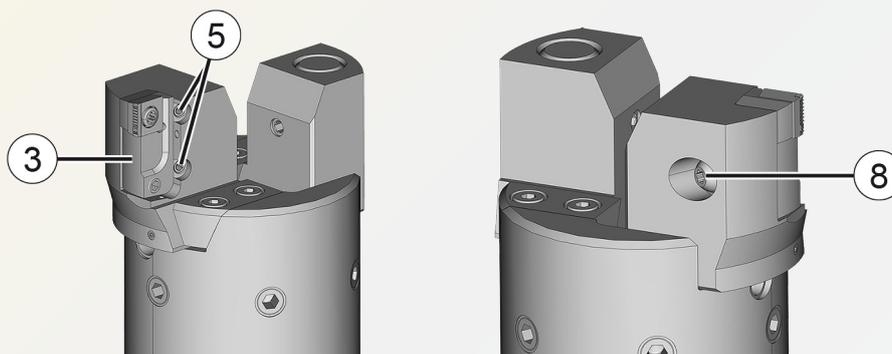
Einstellschrauben Gewindekeilverstellung, Kurzklemmhalter und Kurzklemmhalter Spannschraube
